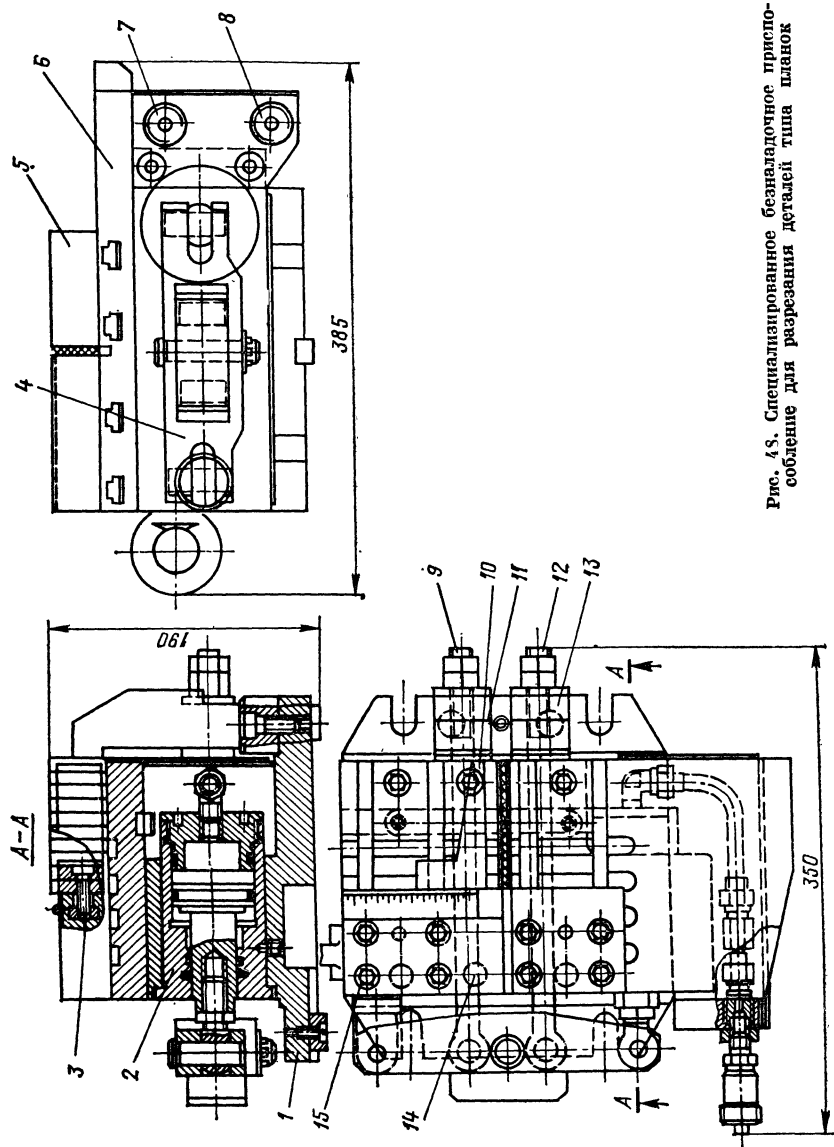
Специализированное безналадочное приспособление для разрезания деталей типа планок
